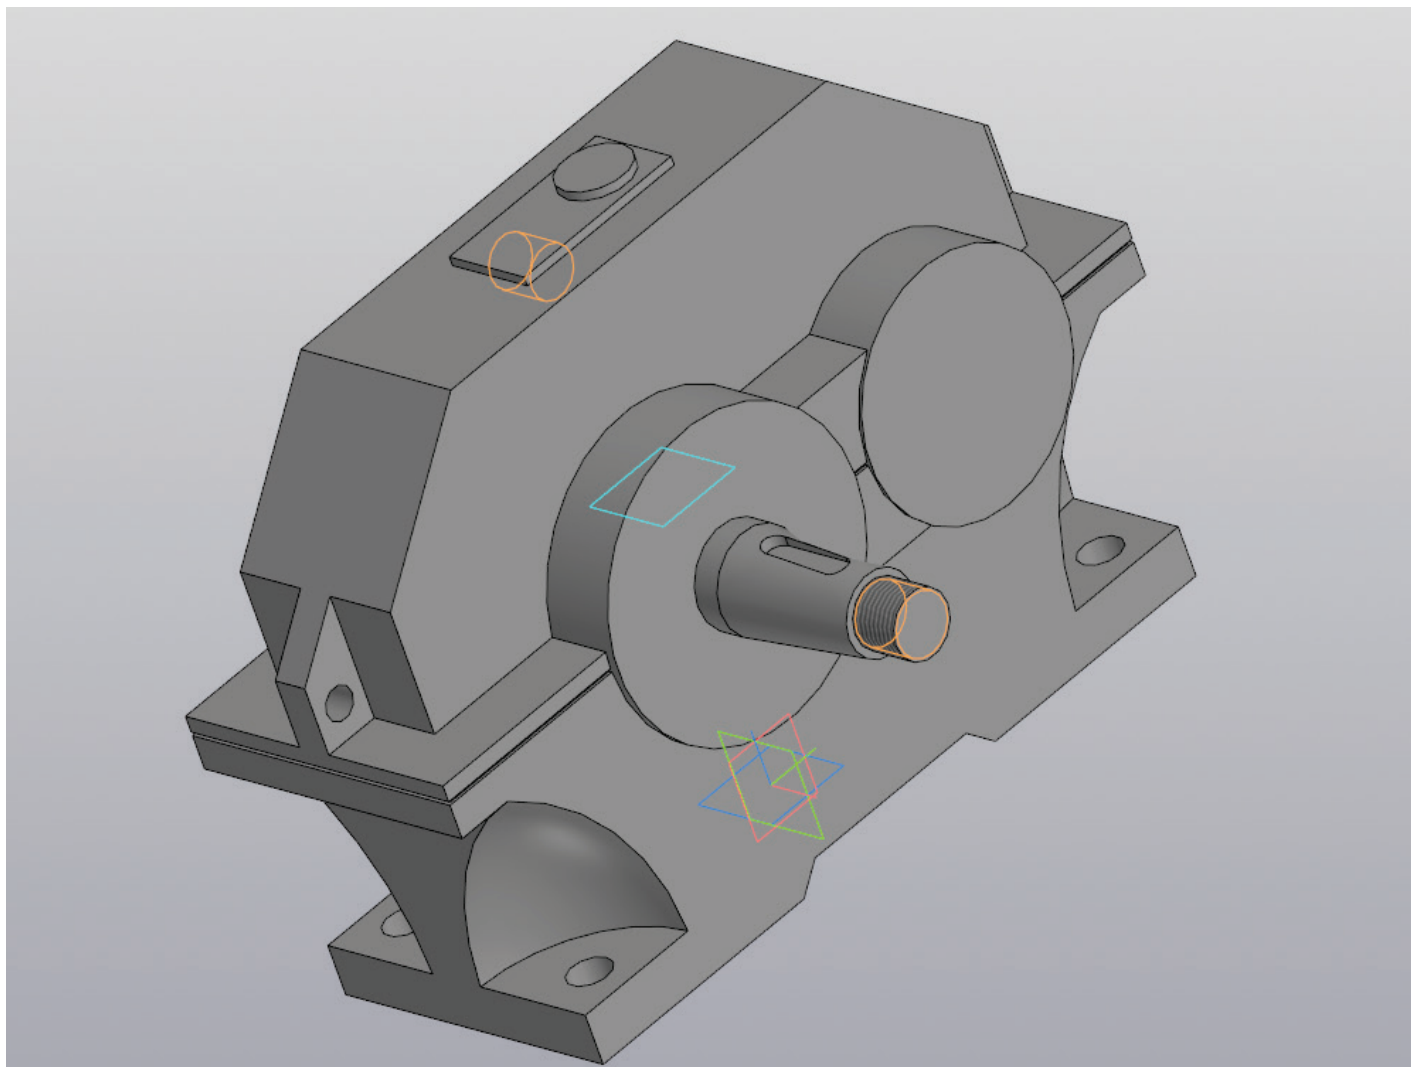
Цилиндрический одноступенчатый редуктор
